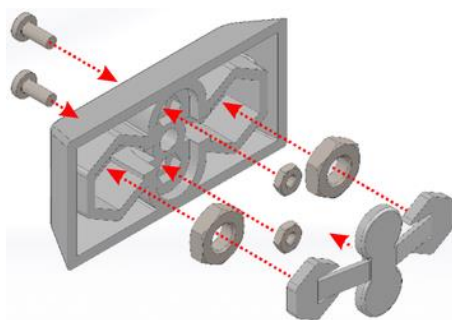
Orden de montaje de los componentes del Mecanismo de Fixação
